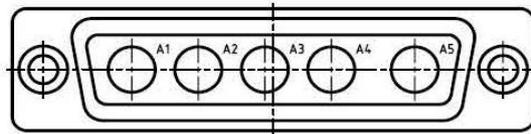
Zeichnung der Power Steckverbindung
